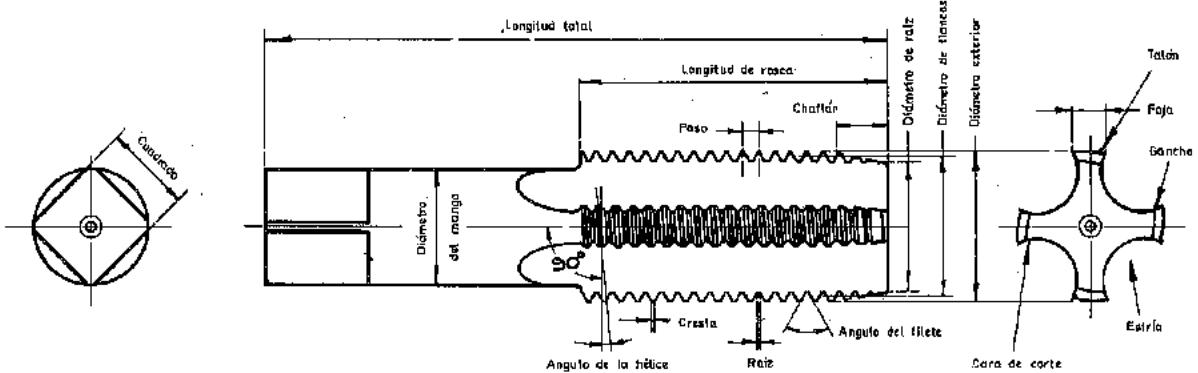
Partes principales de un macho de roscar (Morse Twist Drill & Machine Co.).
